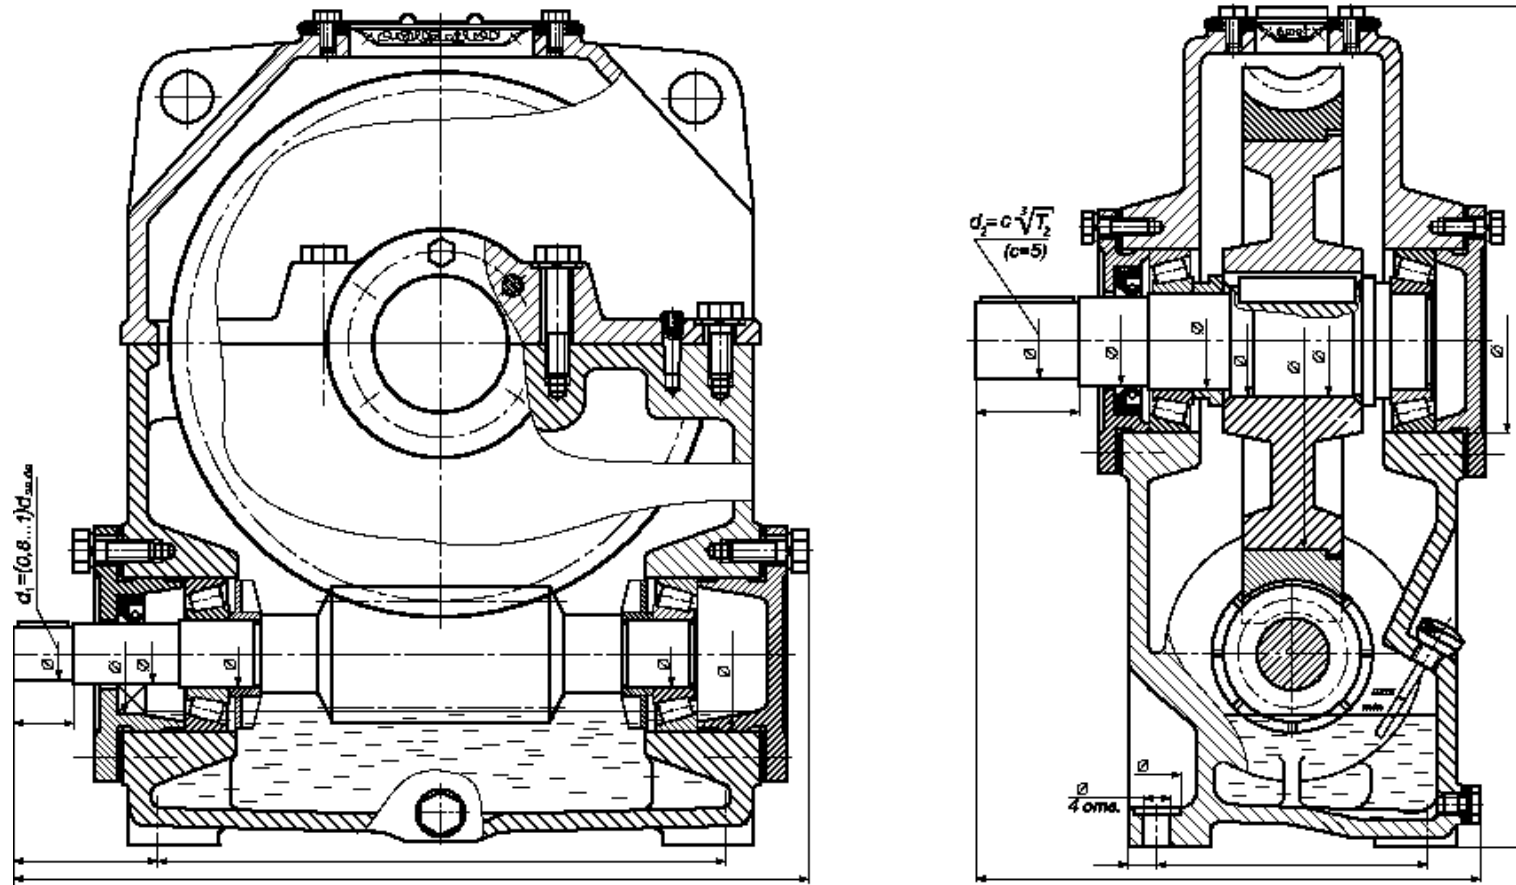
Конструкция червячного редуктора с нижним расположением червяка
